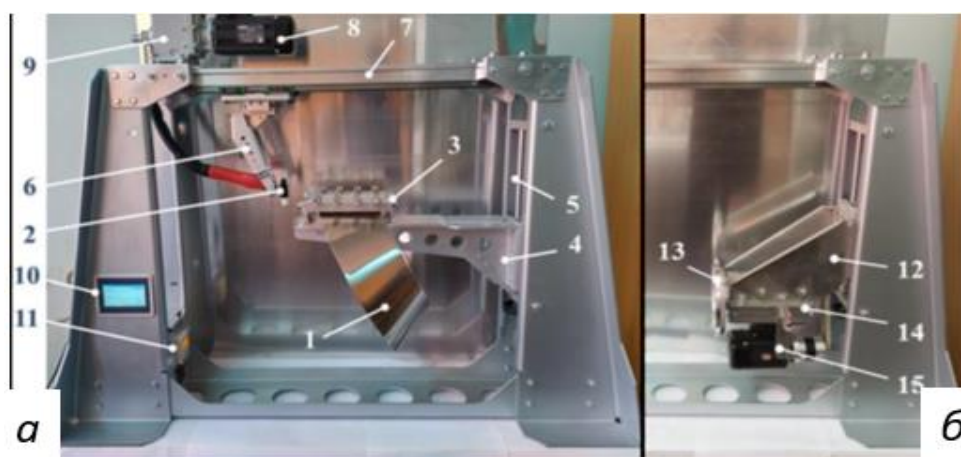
Загальний вигляд установки для зварювання прямолінійних швів у конфігурації з пристосуванням фіксації та захисту кореня шва у процесі зварювання конічної заготовлі секцій КПО (а) та обертач установки для збирання та зварювання кільцевих швів (б)
